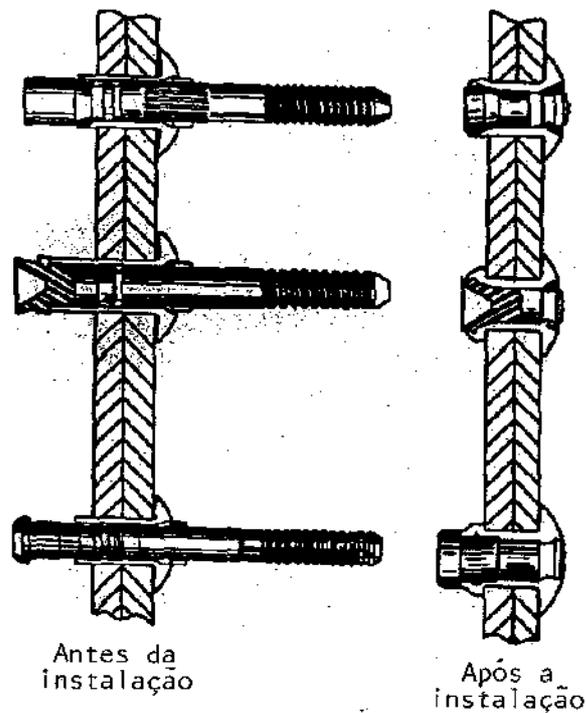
Rebites de auto-cravação (travados mecanicamente).
